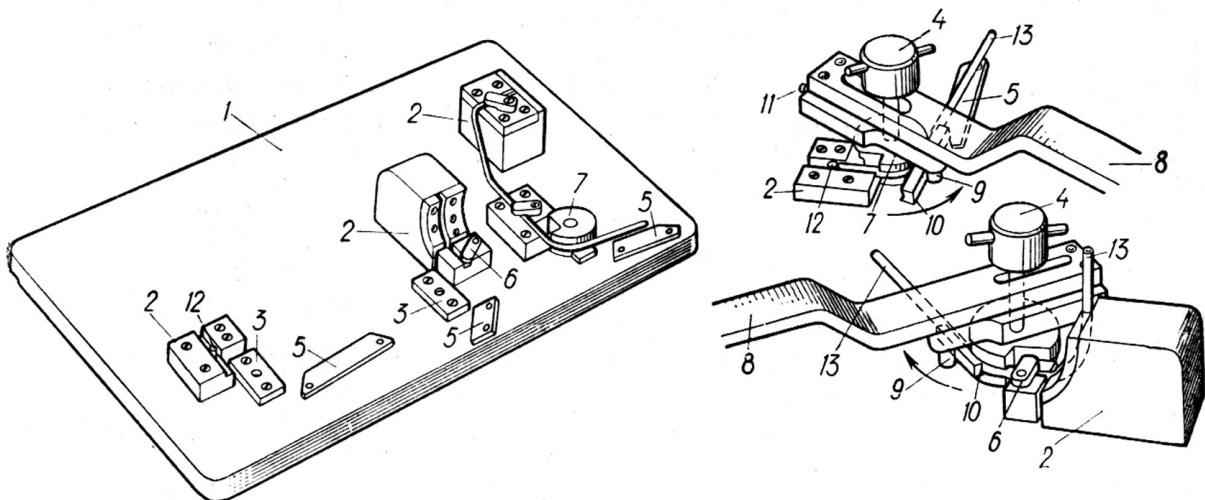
Приспособление для гибки в нескольких плоскостях:
